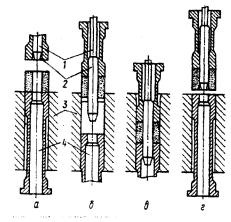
Схема калибрования заготовок типа гладких втулок:
